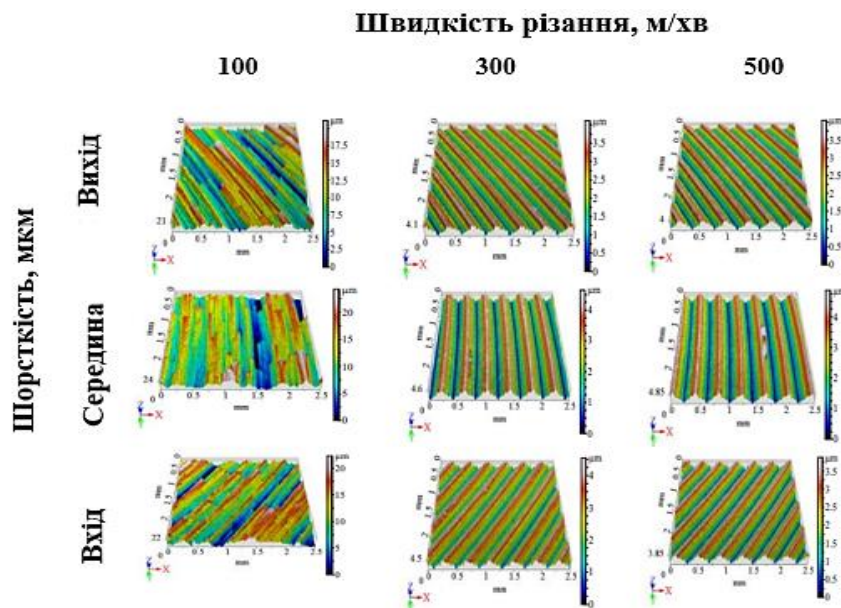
3D-профілі шорсткості поверхні після торцевого фрезерування [41]
